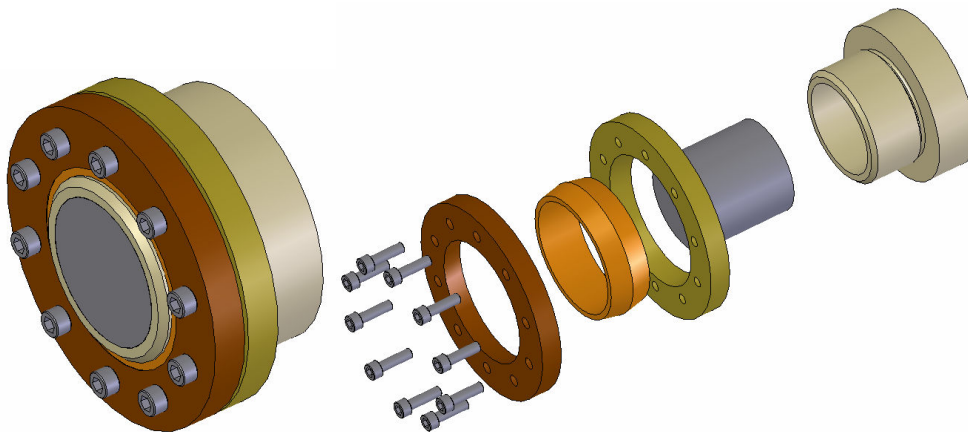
Vue d'ensemble de la frette en position assemblée et vue éclatée de ce même produit.
